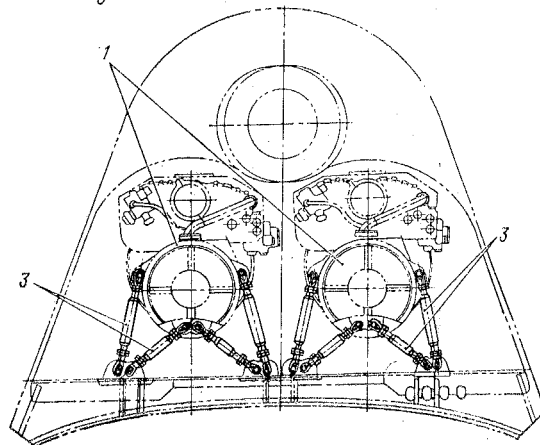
Схема крепления двигателей и редуктора на вертолете:
